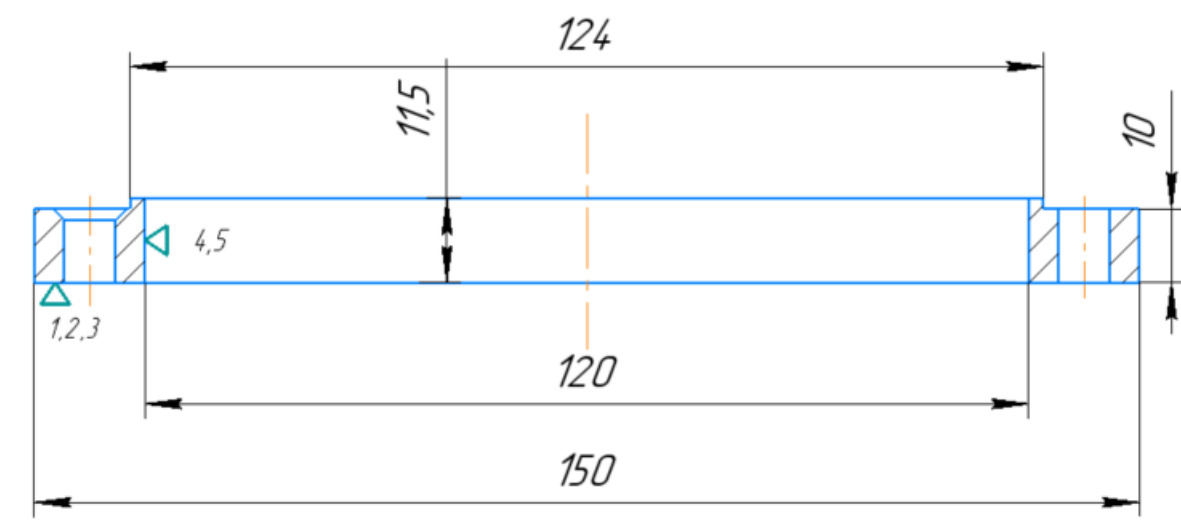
Схема базування заготовки в короткій оправці
